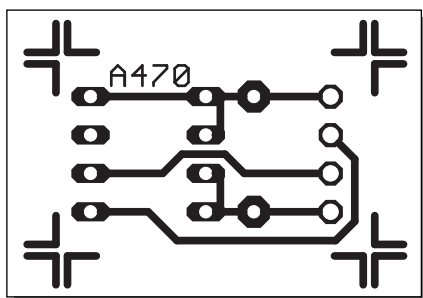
Deska spojů hlavního modulu - BOTTOM
